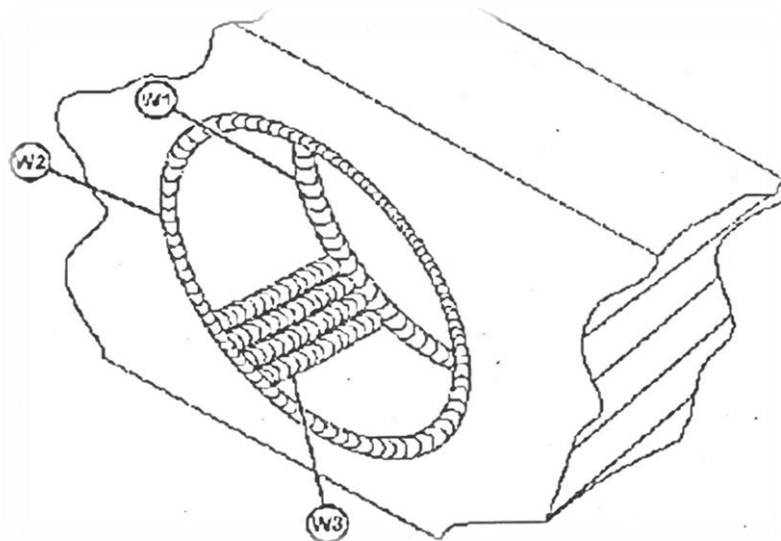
Sequência de soldagem dos furos com passes W1, W2 e W3.
